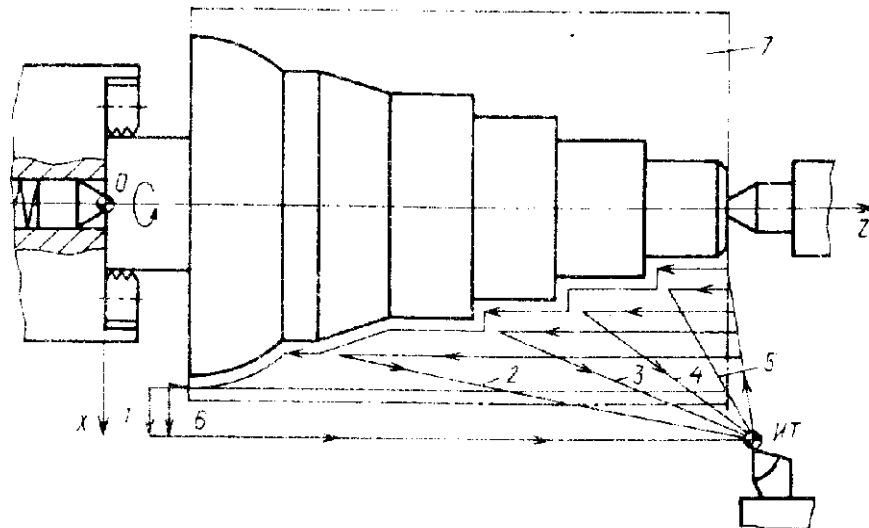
Токарна обробка на верстаті з ЧПК
